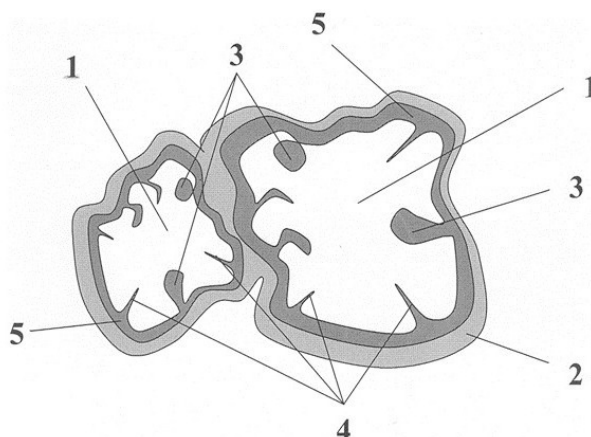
Соединение алмазных зерен 1 – абразивное зерно; 2 – связующий металл; 3 – поры; 4 – трещины; 5 – металл покрытия.
